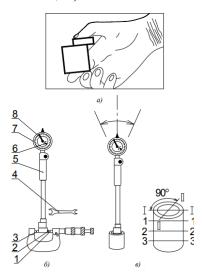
Схема измерения действительных размеров втулки нутромером с индикатором часового типа: а — схема притирки блока концевых
